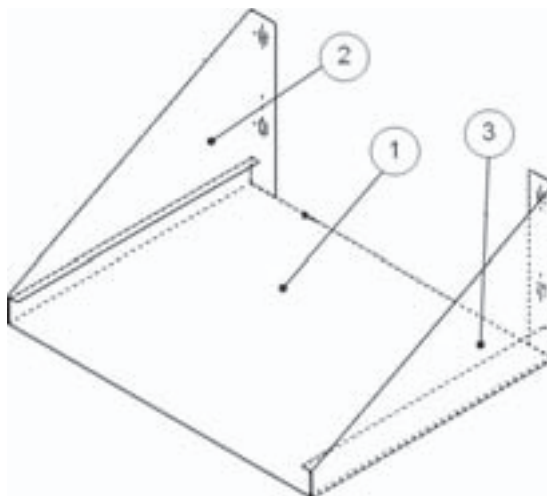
Exemple d'assemblage soudé : support de batterie.
